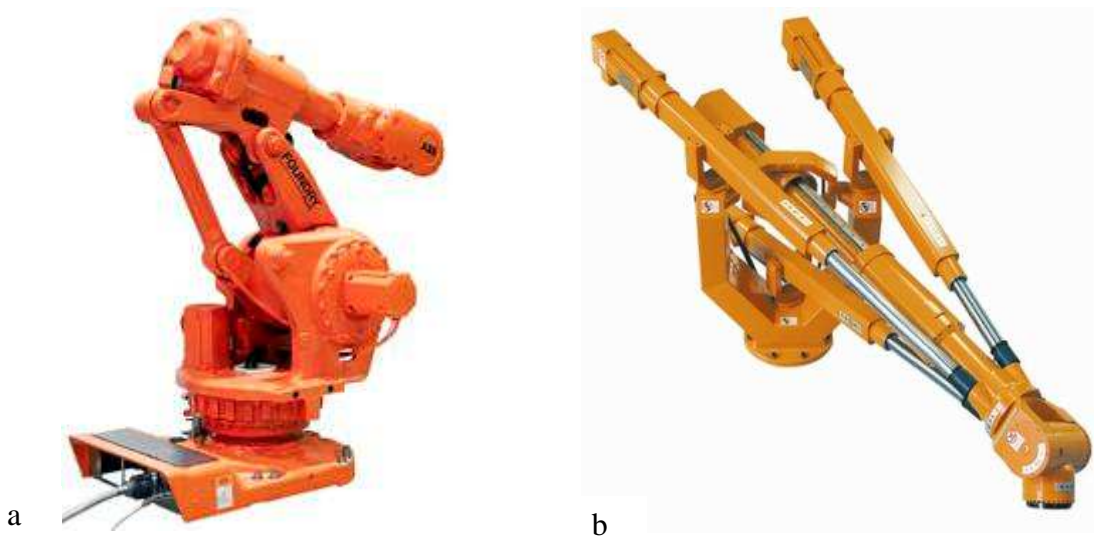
a) robot d'usinage ABB IRB6660 b) robot d'usinage Tricept T606
